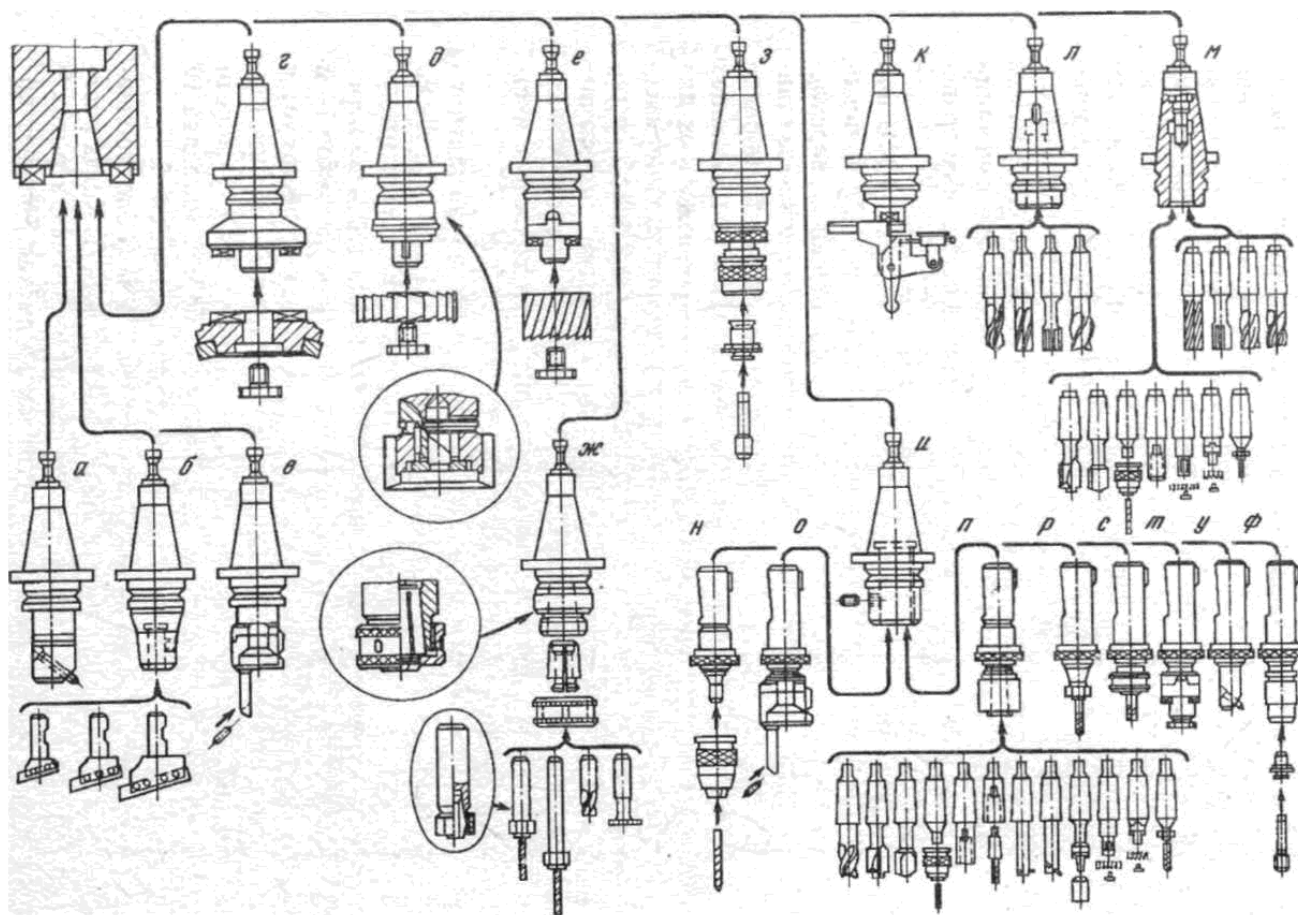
Комплект режущего и вспомогательного инструмента для МЦ.
